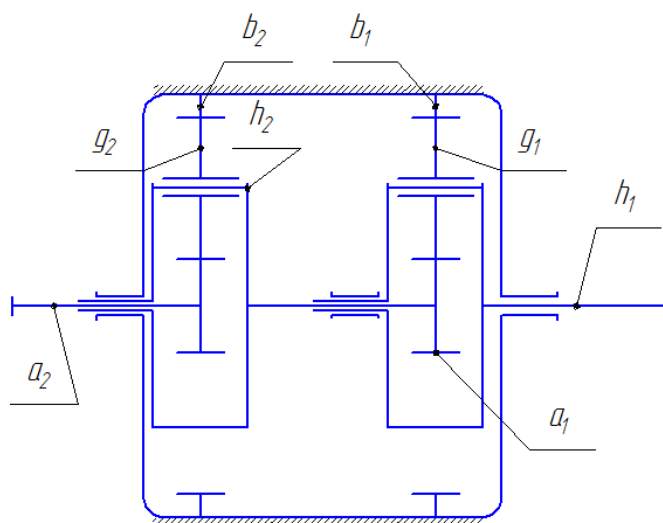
Кинематическая схема двухступенчатого планетарного редуктора для привода цементной мельницы барабанного типа.
